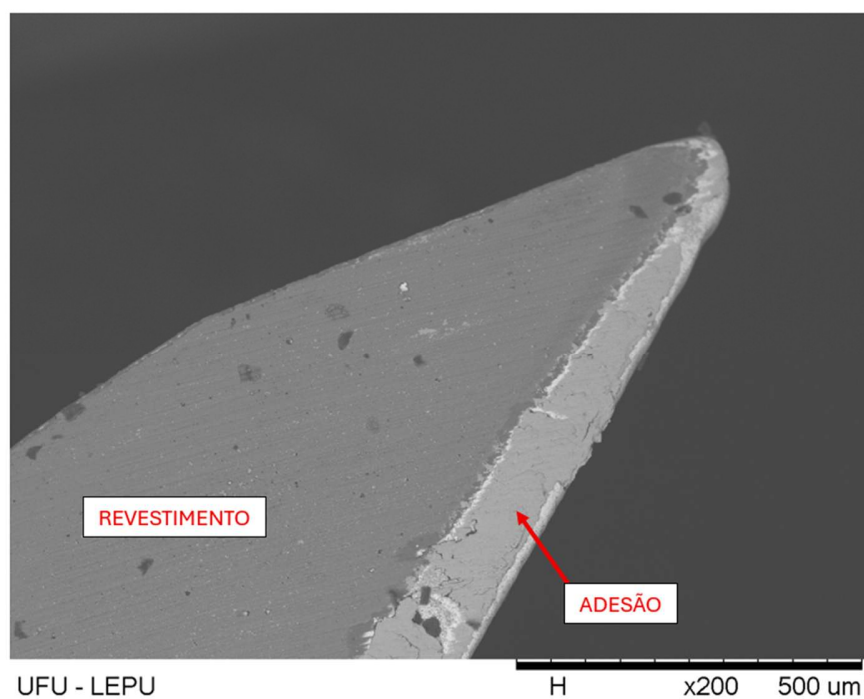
Imagem de MEV da ferramenta revestida R2-C1 (v_c 50 | f_z 0,035) após o ensaio de usinagem.
